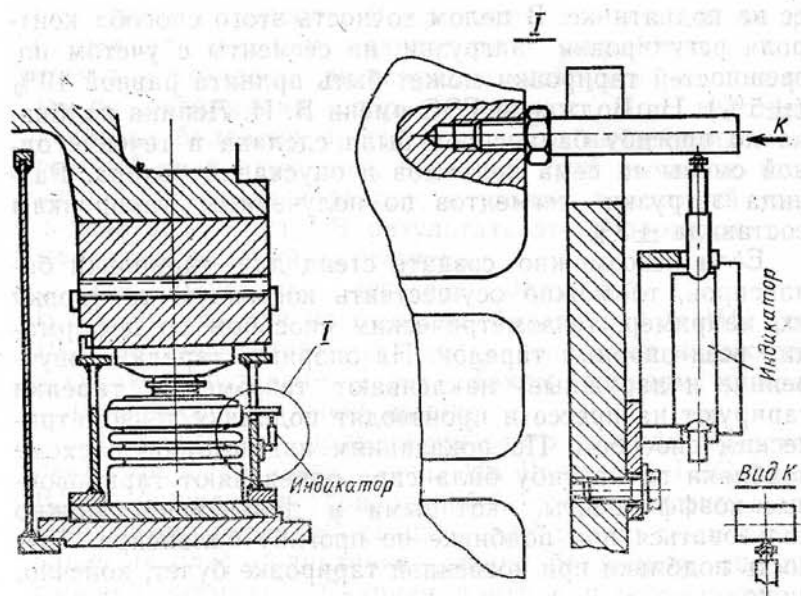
Индикаторное устройство для регулировки высотного положения упругих камер.
